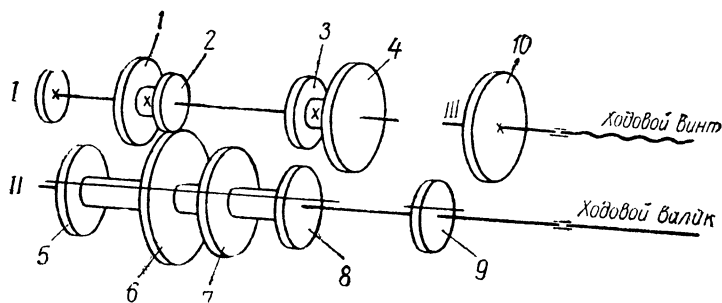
Кинематическая схема коробки подач токарно-винторезного станка модели 1615-М.
